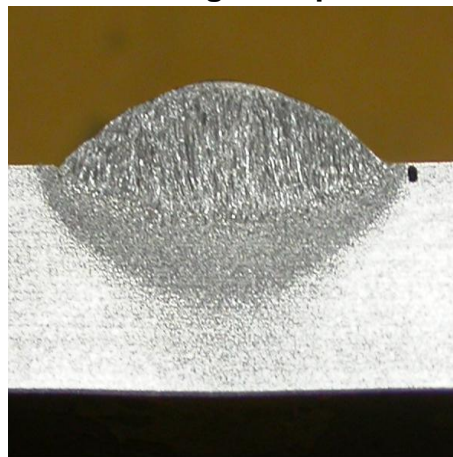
Muestra 2 usando soldadura FCAW con CO₂ como gas de protección
